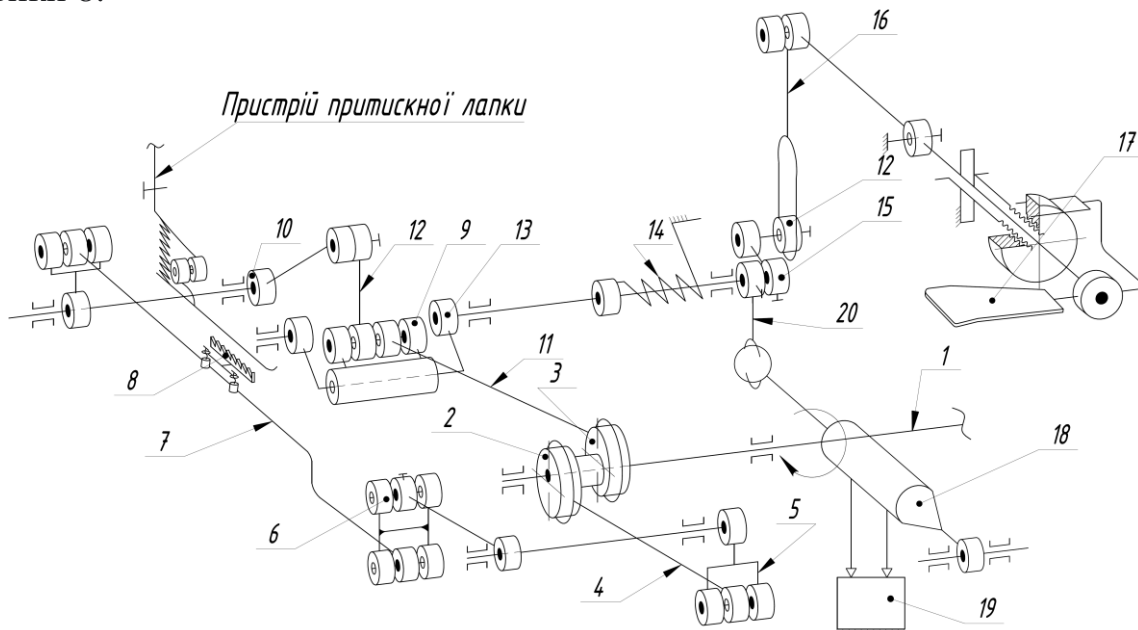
Кінематична схема механізму переміщення матеріалу швейної машини нової конструкції на базі DDL 8700 Juki
